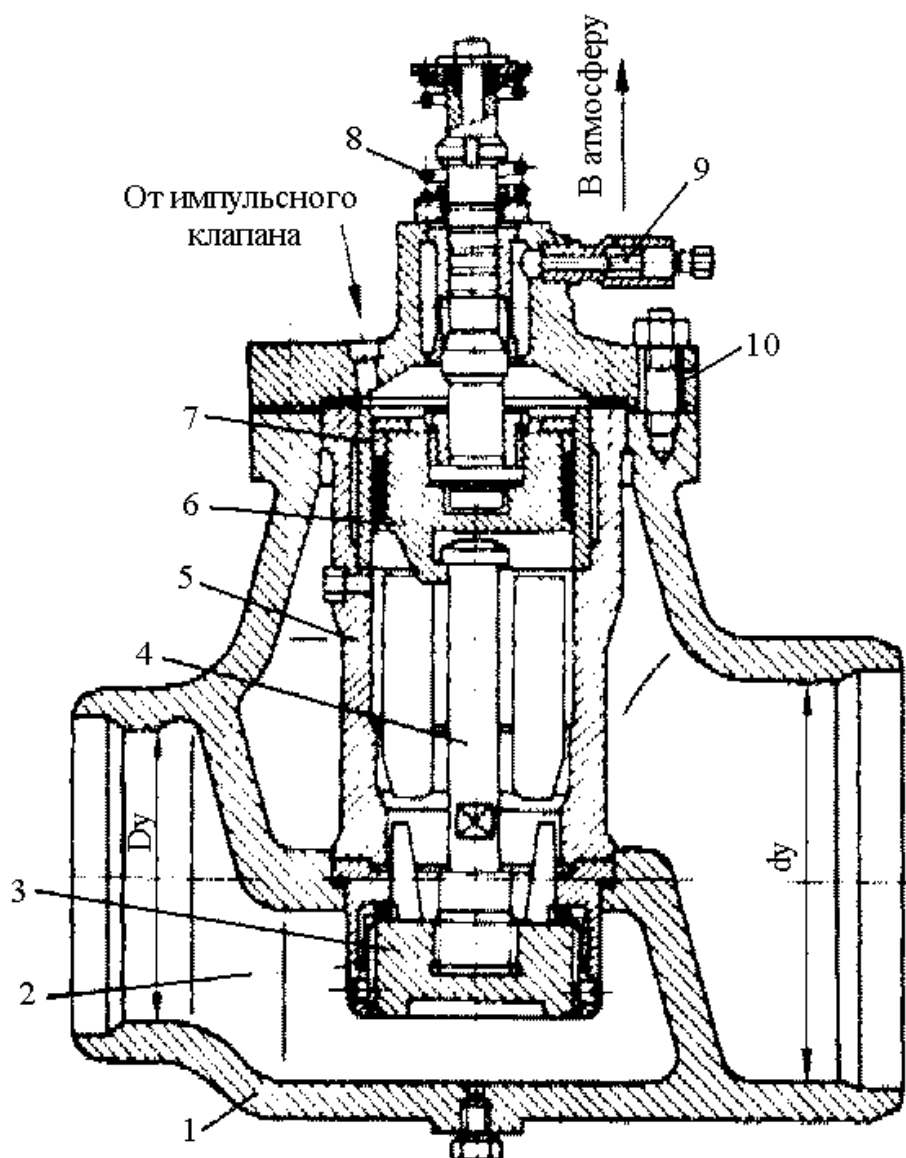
Главный предохранительный клапан линий промежуточного перегрева пара.
